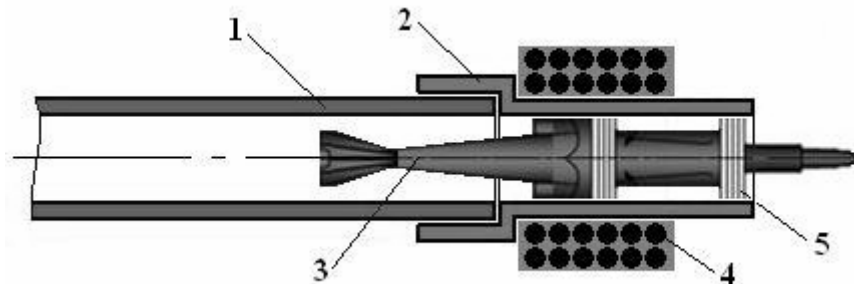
Варіант дообладнання танкової гармати коаксіальним індукційним прискорювачем: 1- ствол, 2 – корпус індуктора, 3 – снаряд, 4 – індуктор, 5 – струмопровідні кільця бронебойно-підкаліберного снаряда
